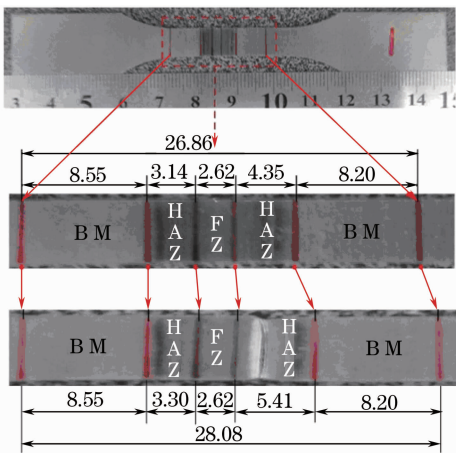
焊接拉伸试验前后接头不同区域的尺寸
